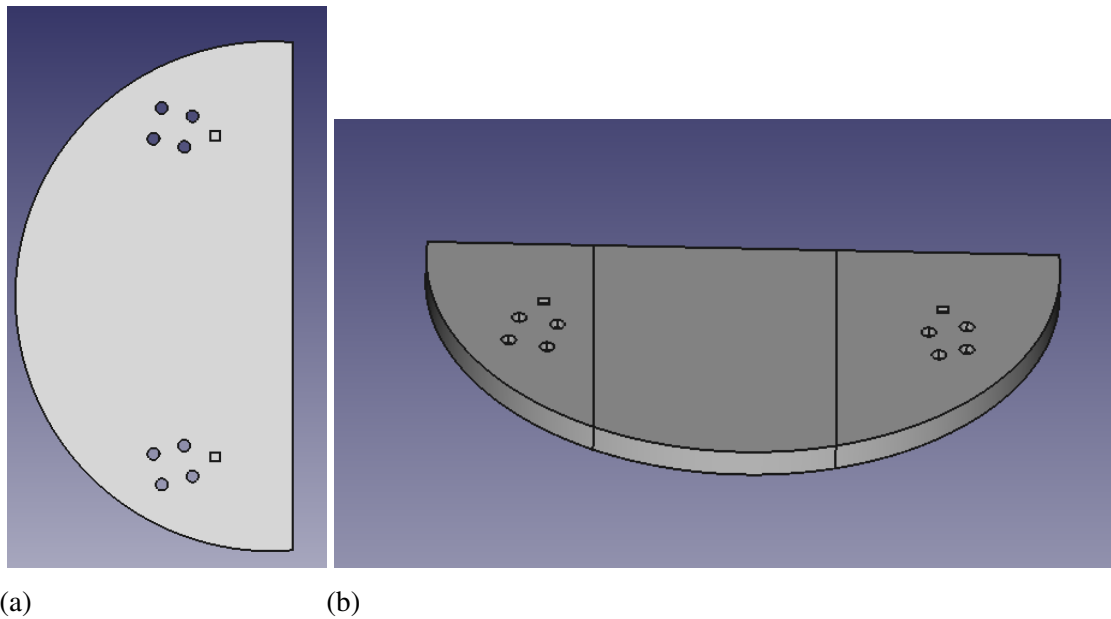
Diseño de la base que une la cabeza con el cuerpo del robot.
